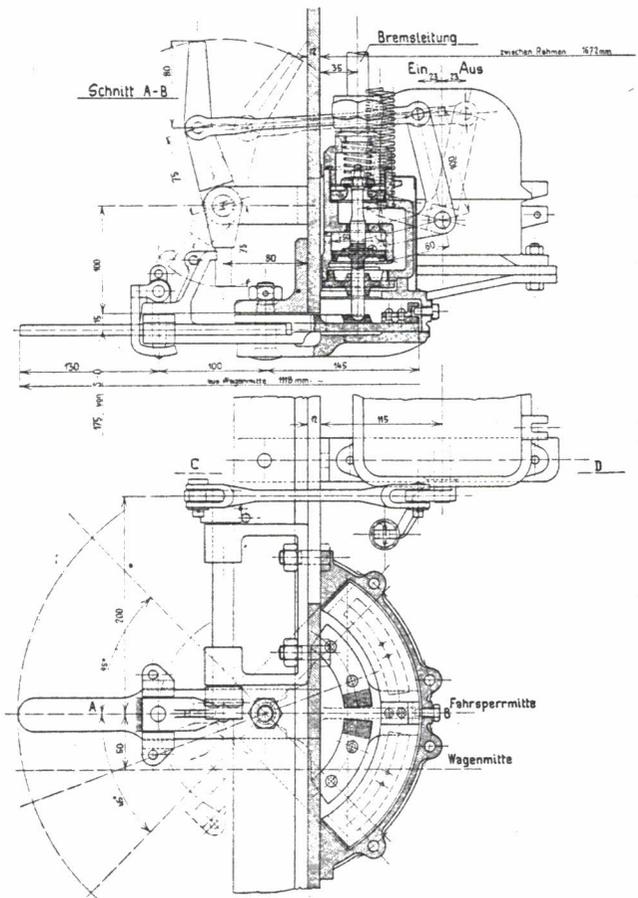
Fahrsperrenausrüstung am Triebwagen.
